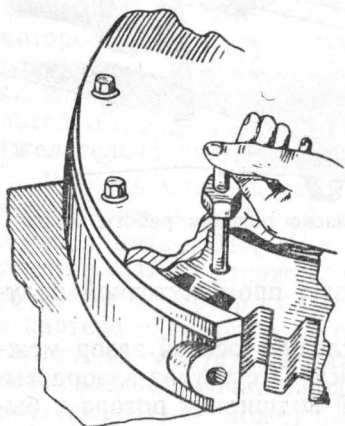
Установка первого цилиндра двигателя ГАЗ-МК в МВТ.
